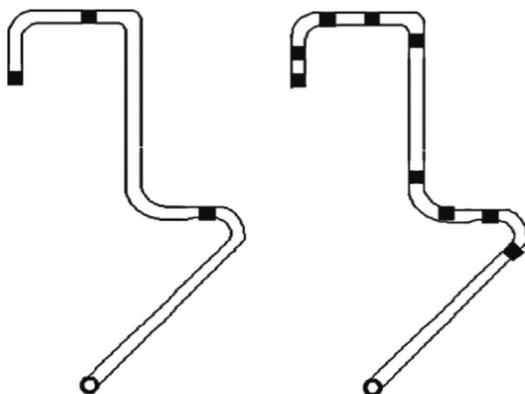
Пример сокращения количества сварных швов для труб с изгибами
